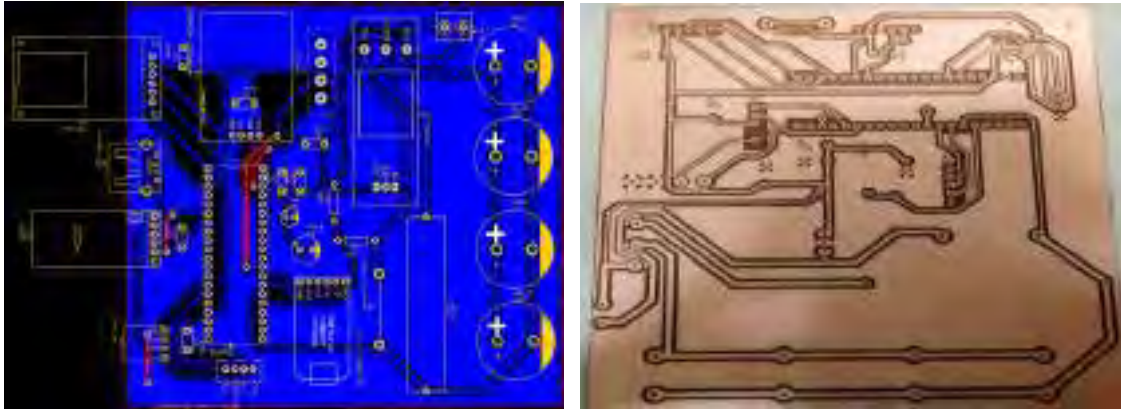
Diseño de la PCB y placa del circuito impreso (Elaboración propia).
